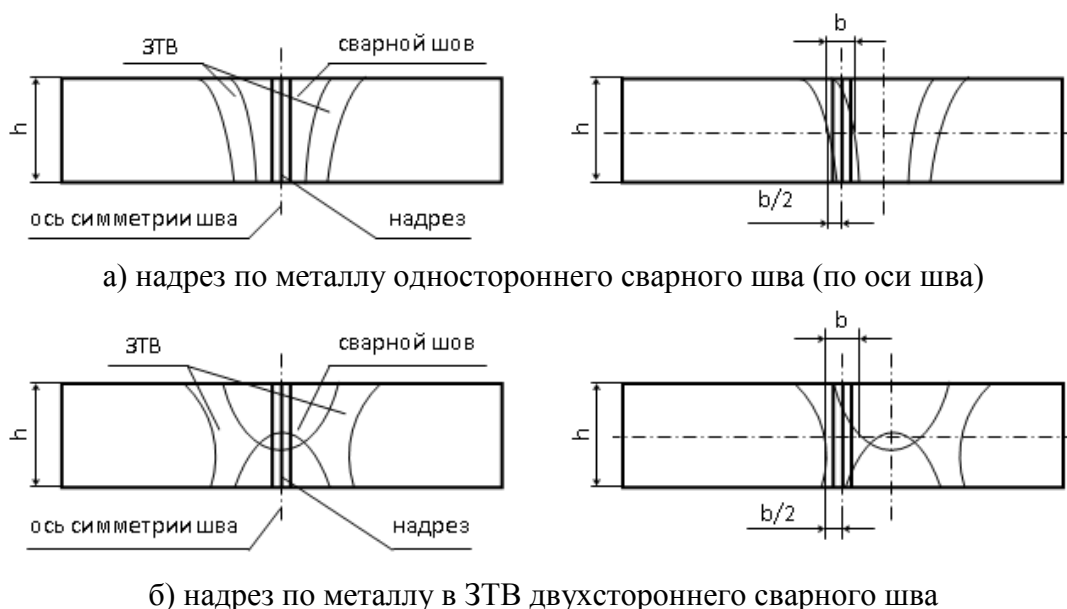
Схема выполнения надреза на образцах для испытаний на ударный изгиб
